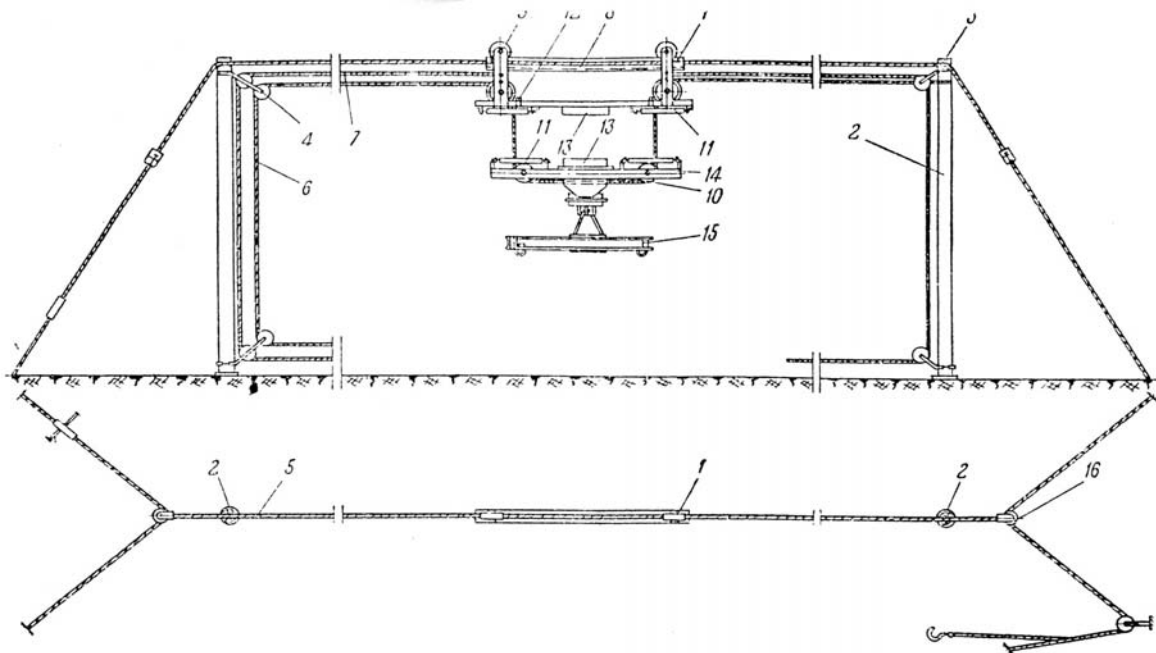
Типова схема кабель-крана для навантажувально-розвантажувальних робіт [1]: 1 – вантажна каретка з вантажозахоплювальним пристроєм; 2 – щогла кабель-крана; 3 – наголовники; 4 – напрямні блоки; 5 – несучий канат; 6 – вантажний канат; 7 – тяговий канат; 8 – рама візка; 9 – їздові ролики; 10 – блок; 11 – ролики напрямні; 12 – ролик обмежувачий; 13 – буфер; 14 – рама підвіски; 15 – коромисло; 16 – блоки 10-тонні
